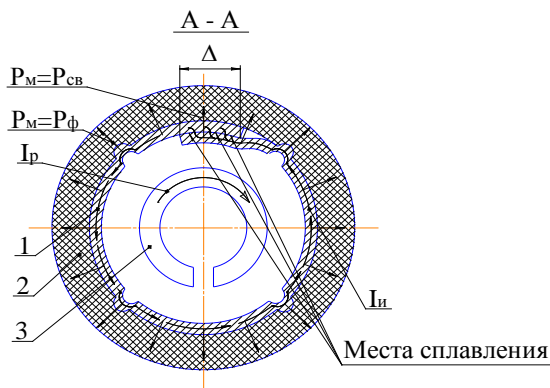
Эскиз экранирующего корпуса-соединителя.
